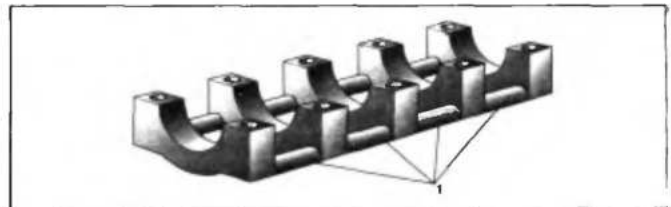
Крышки коренных подшипников, выполненные как одна деталь:
